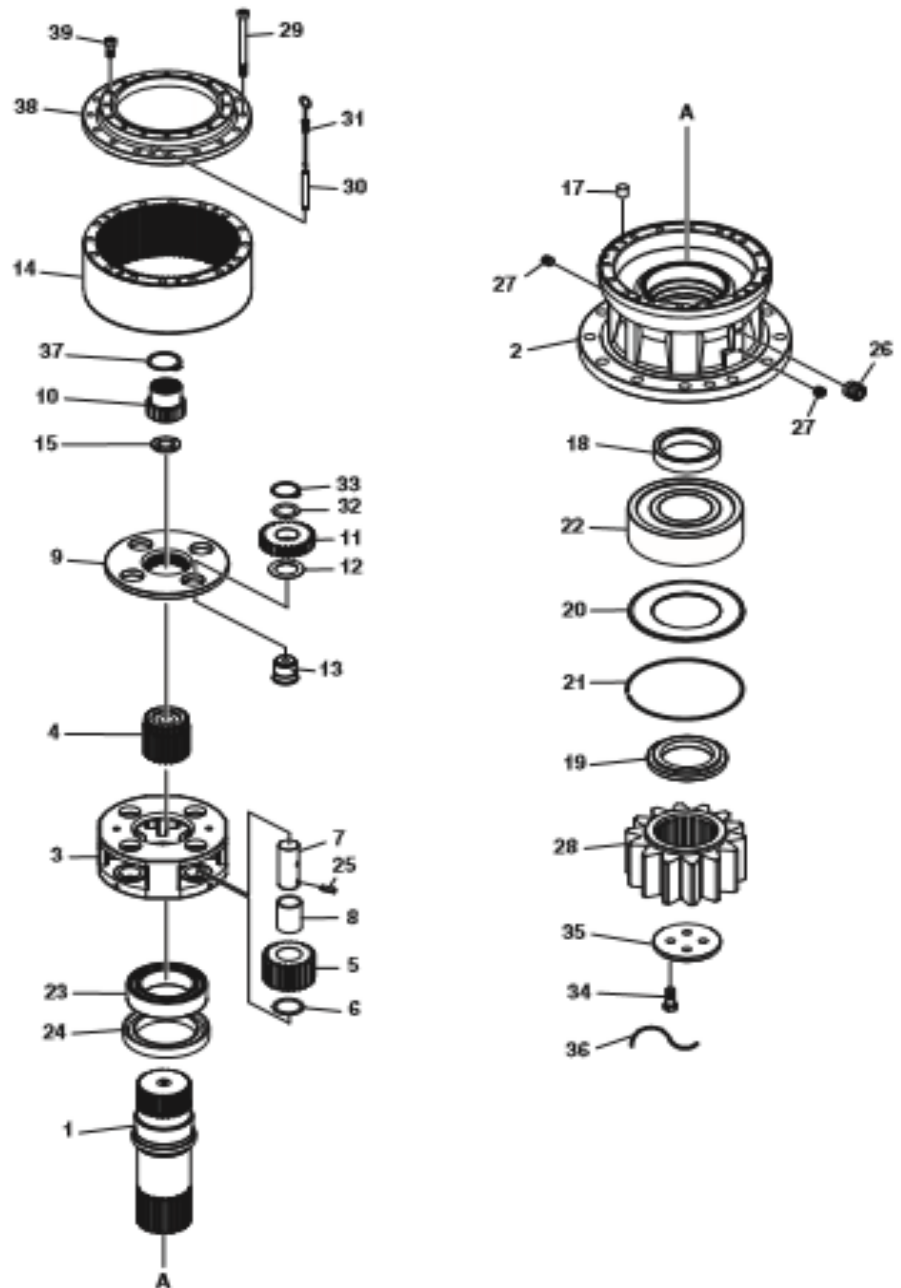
Swing gear reduction Doosan excavator DX300LCA.
